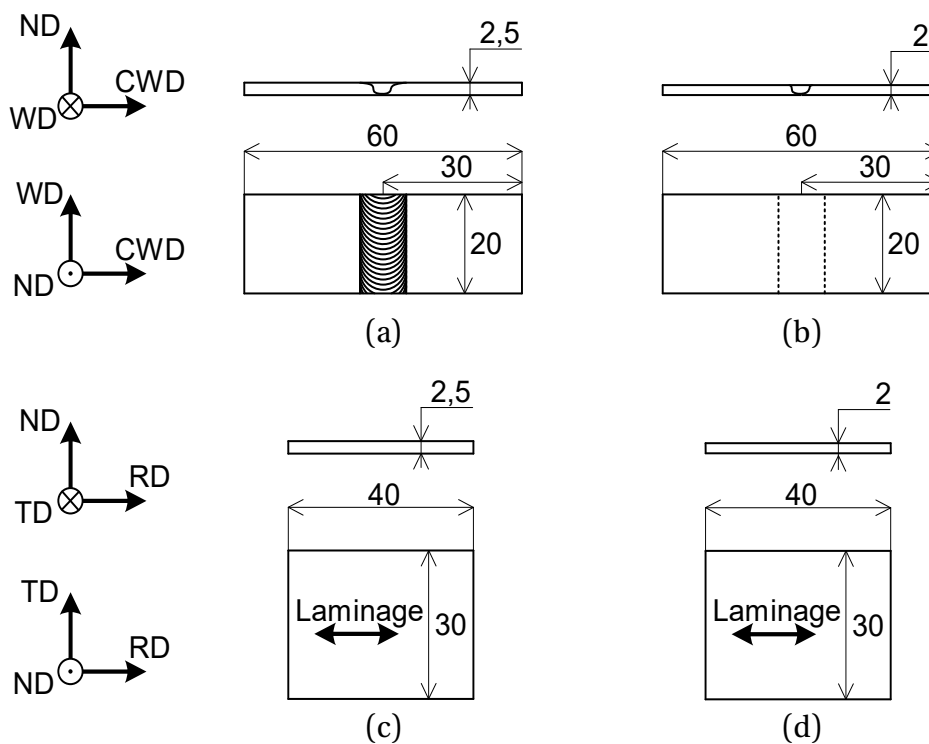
Géométrie des éprouvettes de corrosion (a) tôles soudées, éprouvette brute, (b) tôles soudées, éprouvette polie, (c) matériau de base, éprouvette brute, (d) matériau de base, éprouvette polie.
